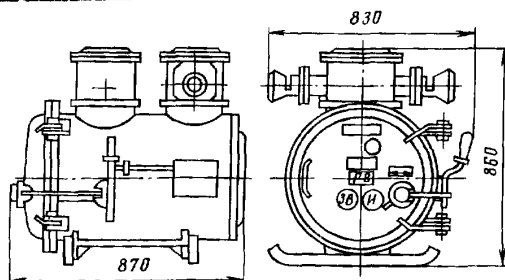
Габаритные размеры пускателя ПВИ-250БТ
